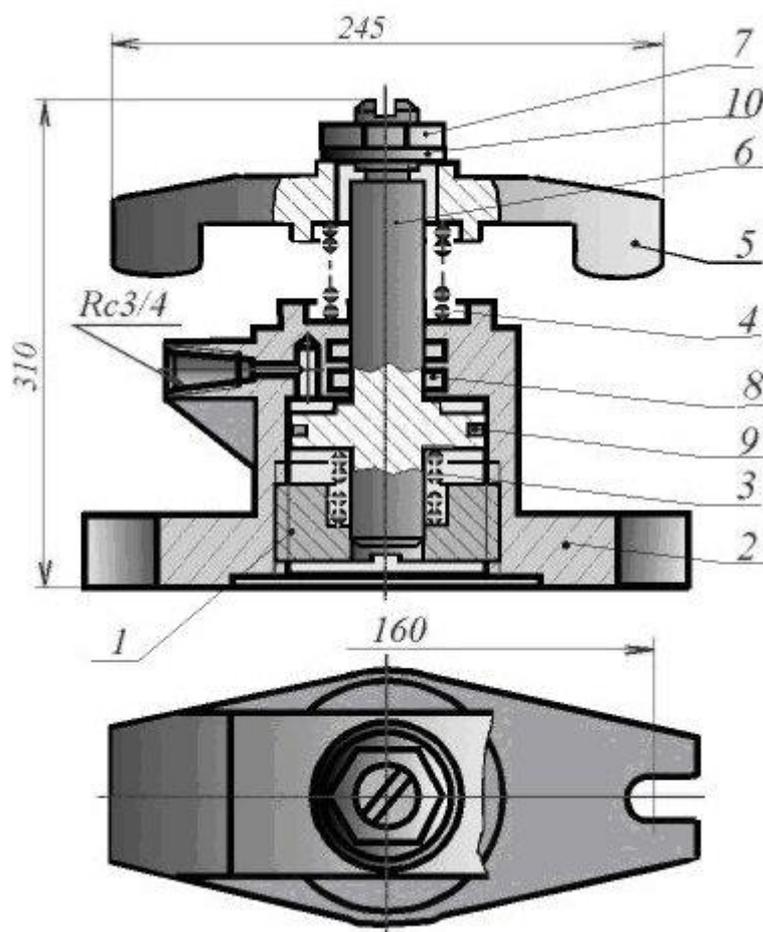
Прихват гидравлический (сборочный чертеж)
